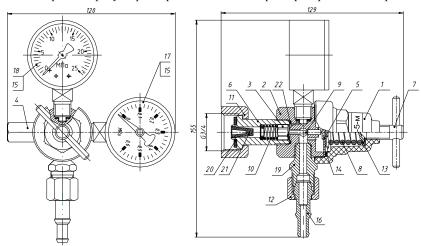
Редуктор баллонный газовый одноступенчатый.
